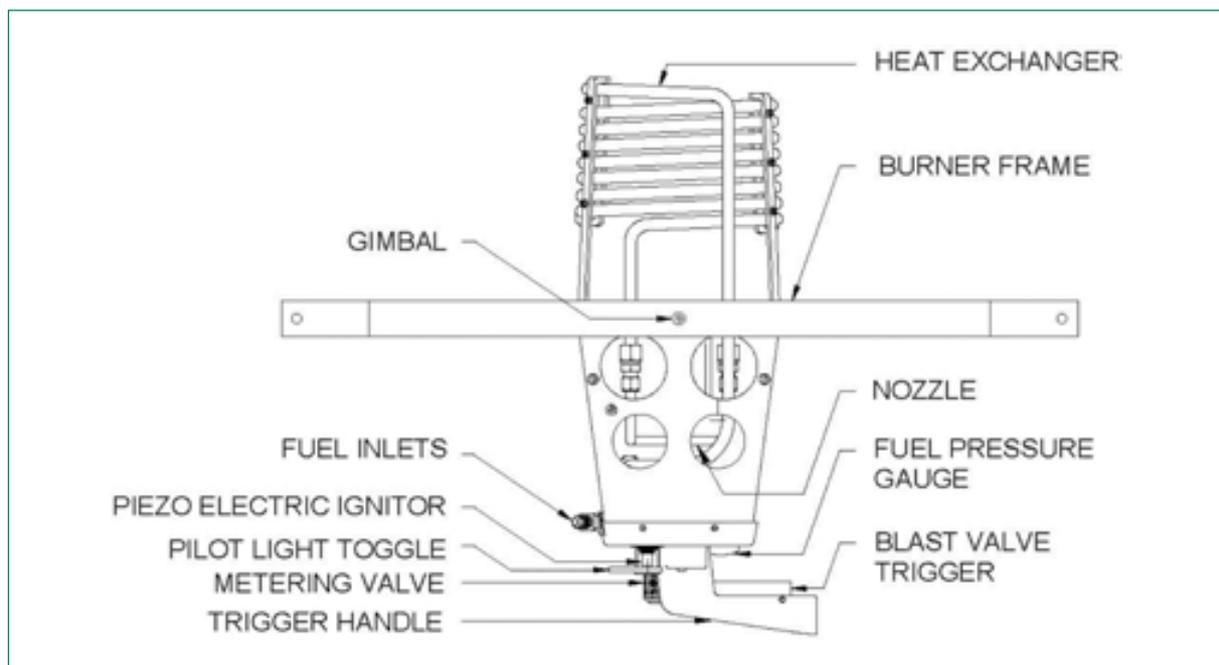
Esquema de un quemador muy parecido al que iba a bordo. Las tuberías de combustible (*fuel inlets*) llegan a la parte inferior izquierda del quemador y se enroscan mediante racores que hay que apretar con una llave fija
